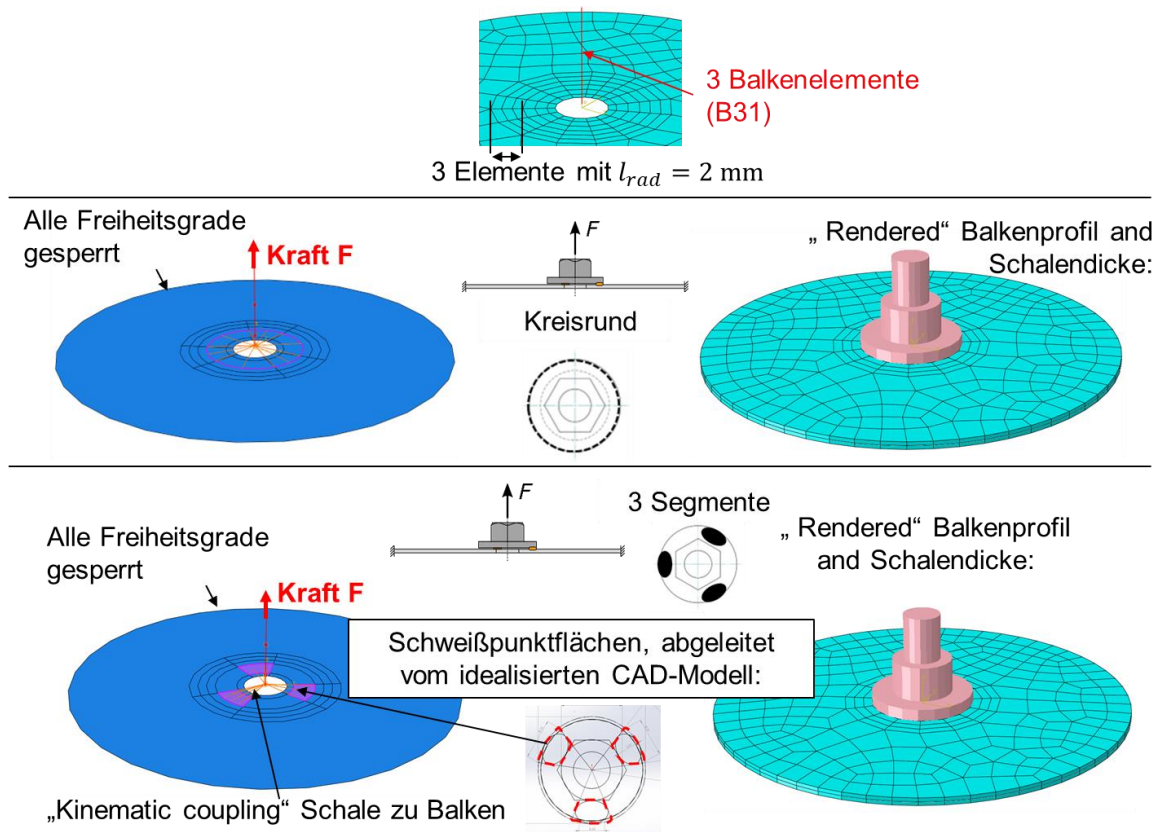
FE-Modelle der Mutterproben mit kreisrunder Schweißnaht und Punktschweißungen mit drei Segmenten, Axialzug
